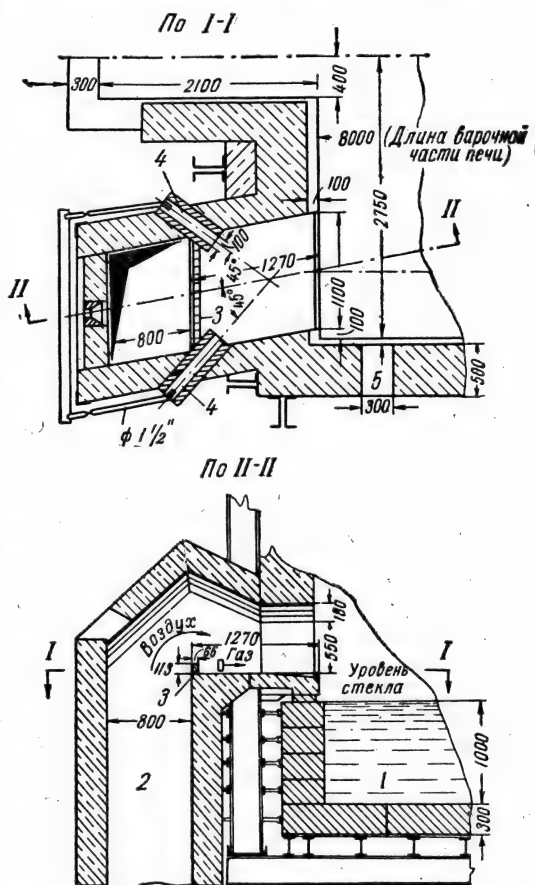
Переоборудование на газовое топливо стекловаренной печи с подковообразным движением пламени:
